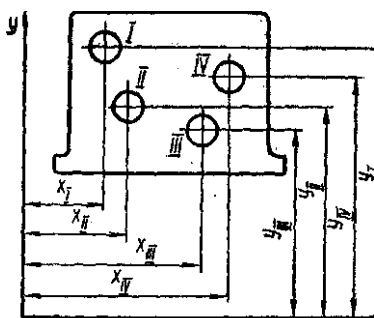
Визначення координат отворів корпусної деталі при обробці на верстатах.
